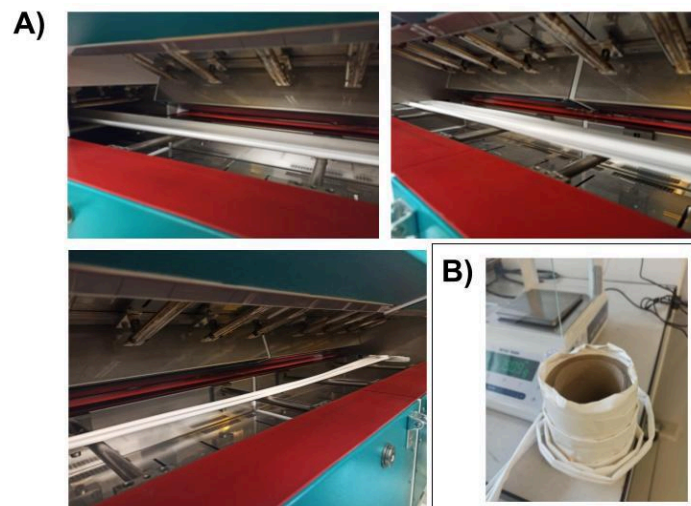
A) CNC/ChNF- Dispersion beschichtetes Papier in der Heißlufttrocknung. B) Getrocknetes und beschichtetes Papier aufgerollt.
